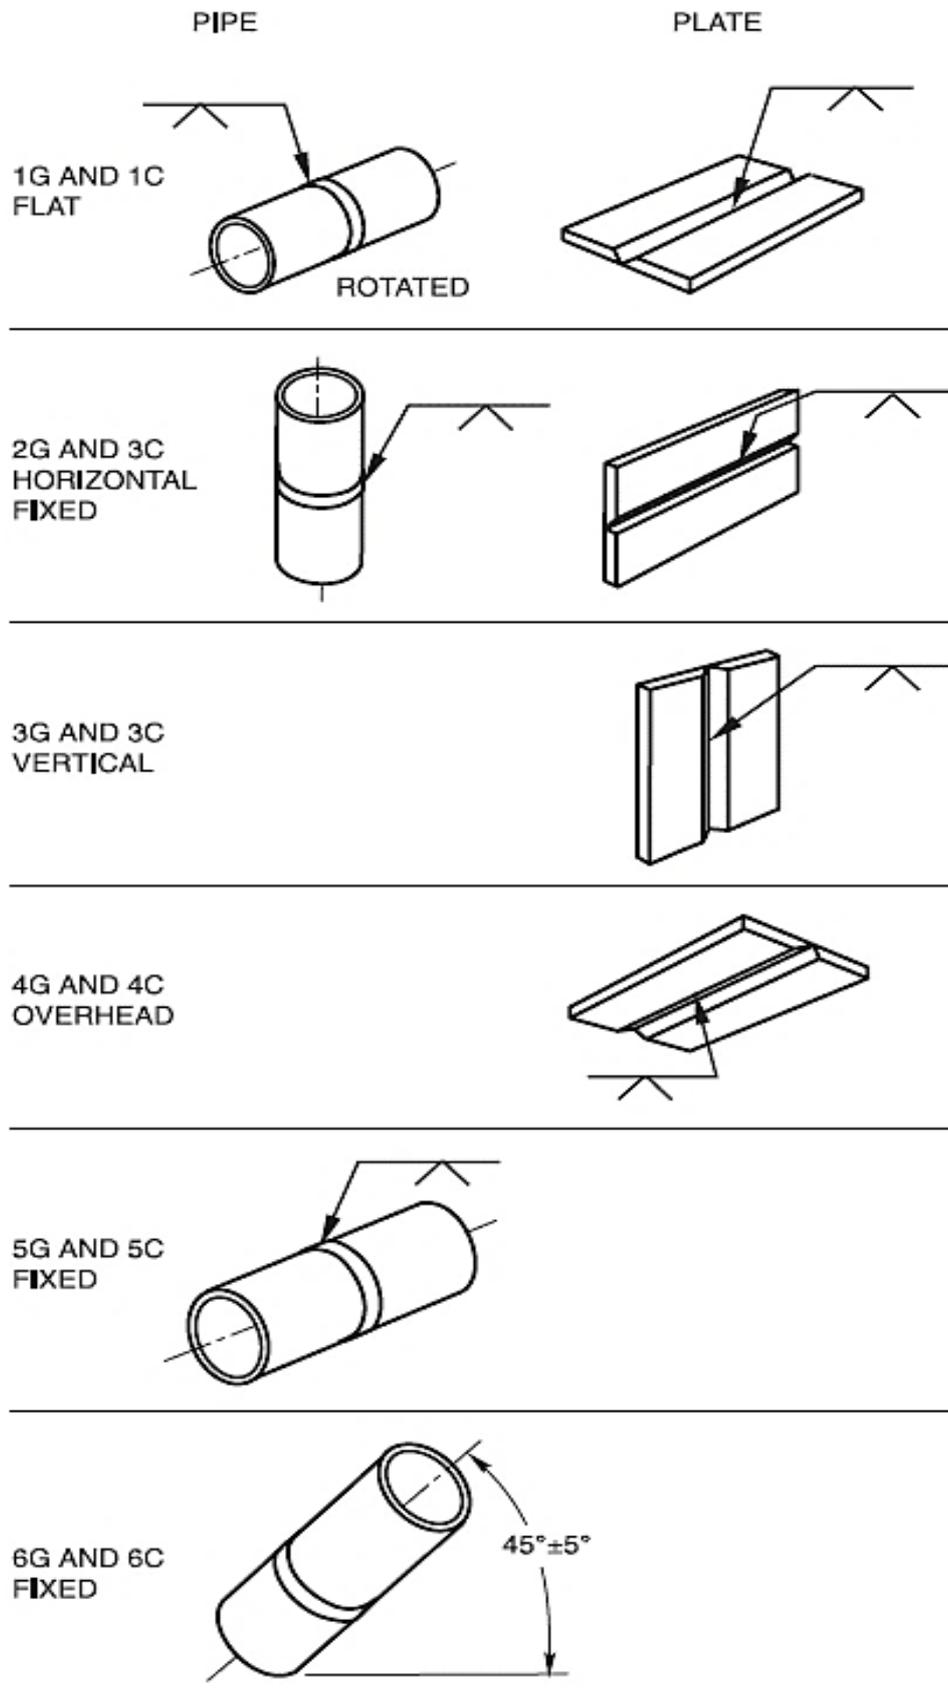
Posiciones para pruebas de soldadura a Tope.
